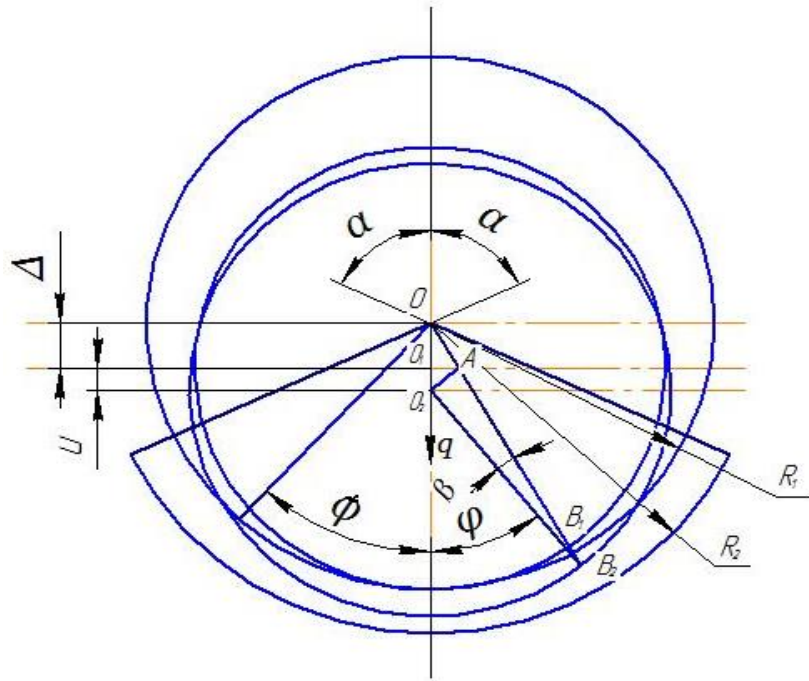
Розрахункова схема переміщення підшипника на податливому металополімерному матеріалі.
